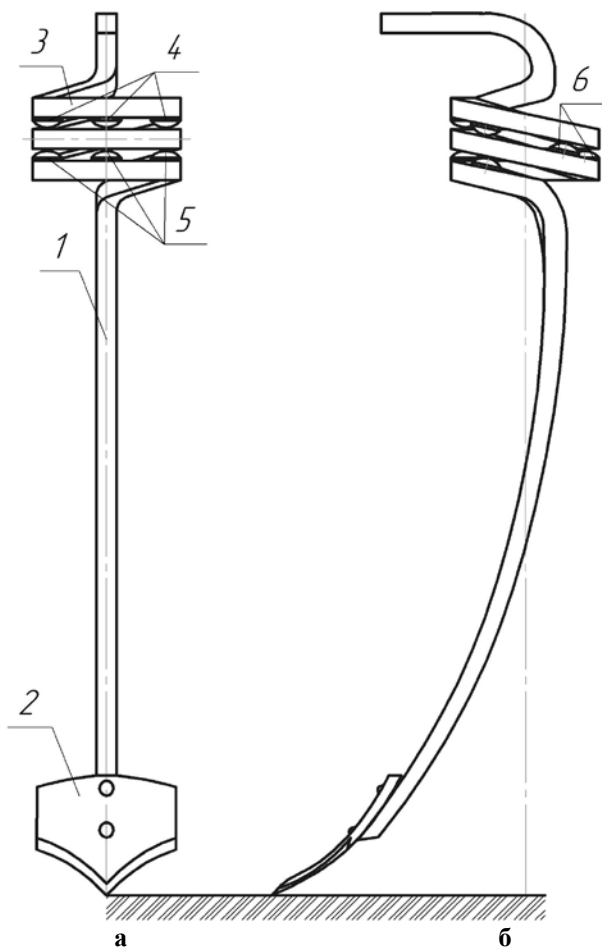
Общий вид рабочего органа культиватора: а) вид спереди; б) вид сбоку.
